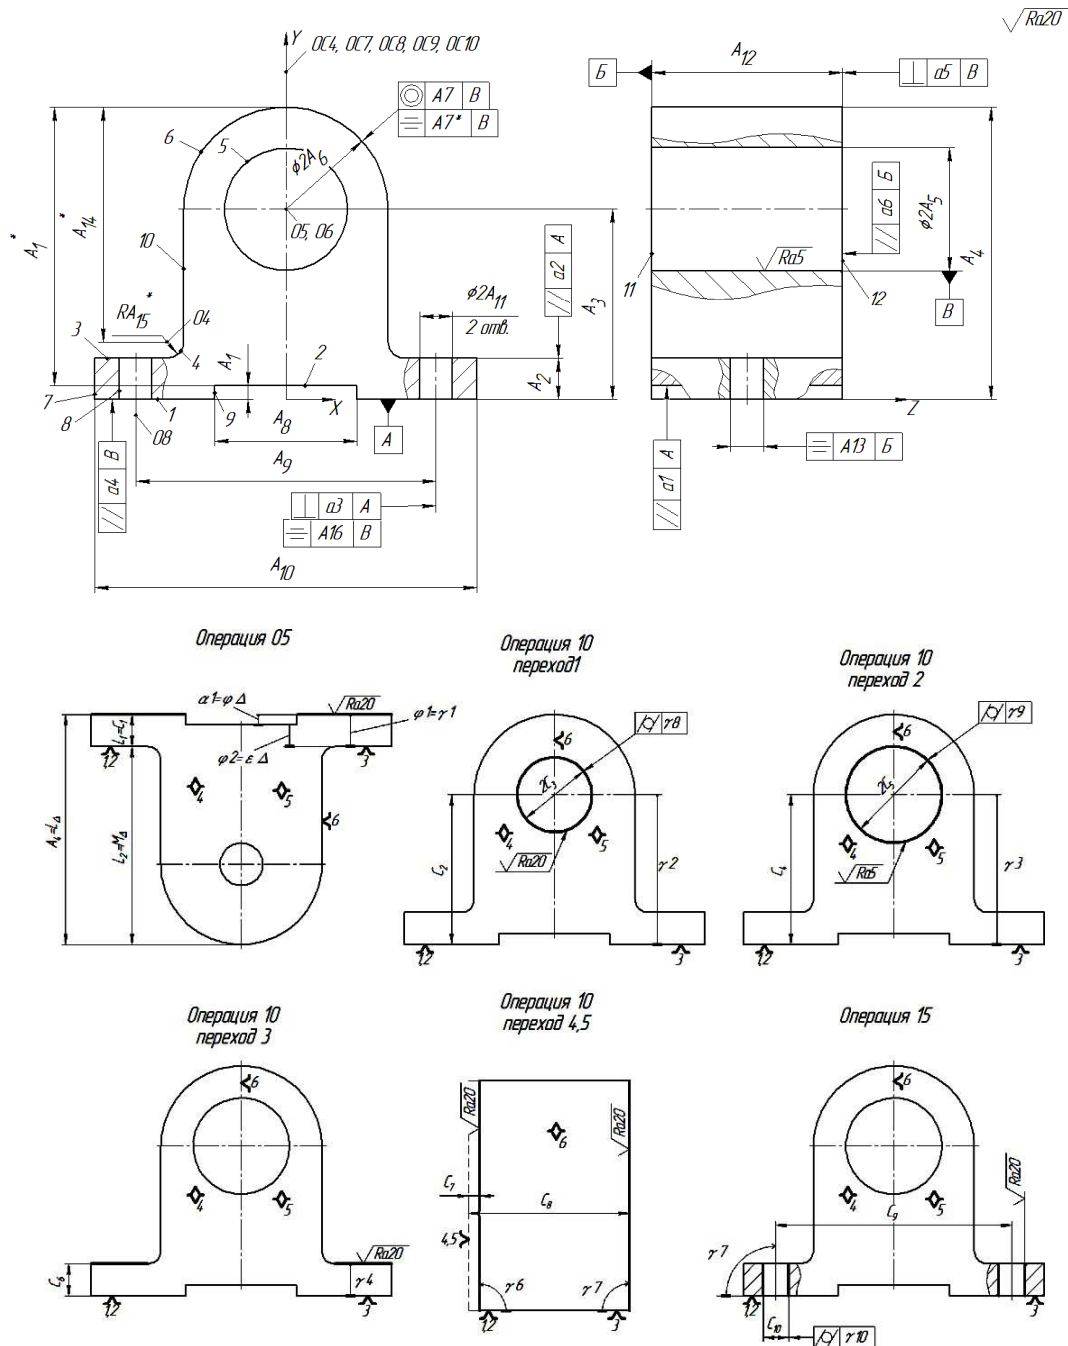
Чертеж детали «корпус» и операционные эскизы ее обработки
